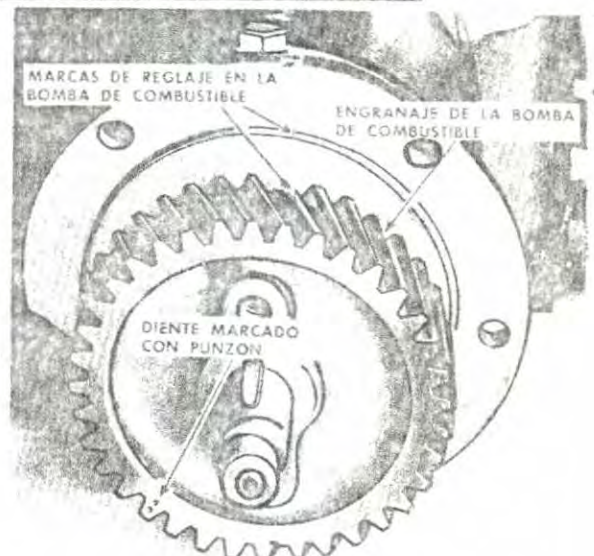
Marcas de reglaje en la bomba de combustible y engranaje.
